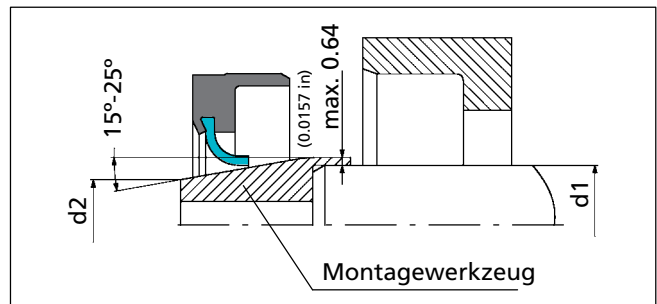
Montage der Dichtlippe mit einem Montagewerkzeug.
